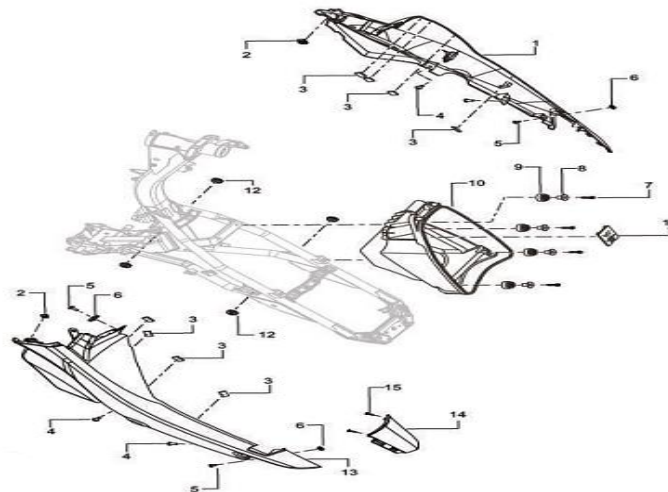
CUBIERTAS SILLÍN- BAÚL
